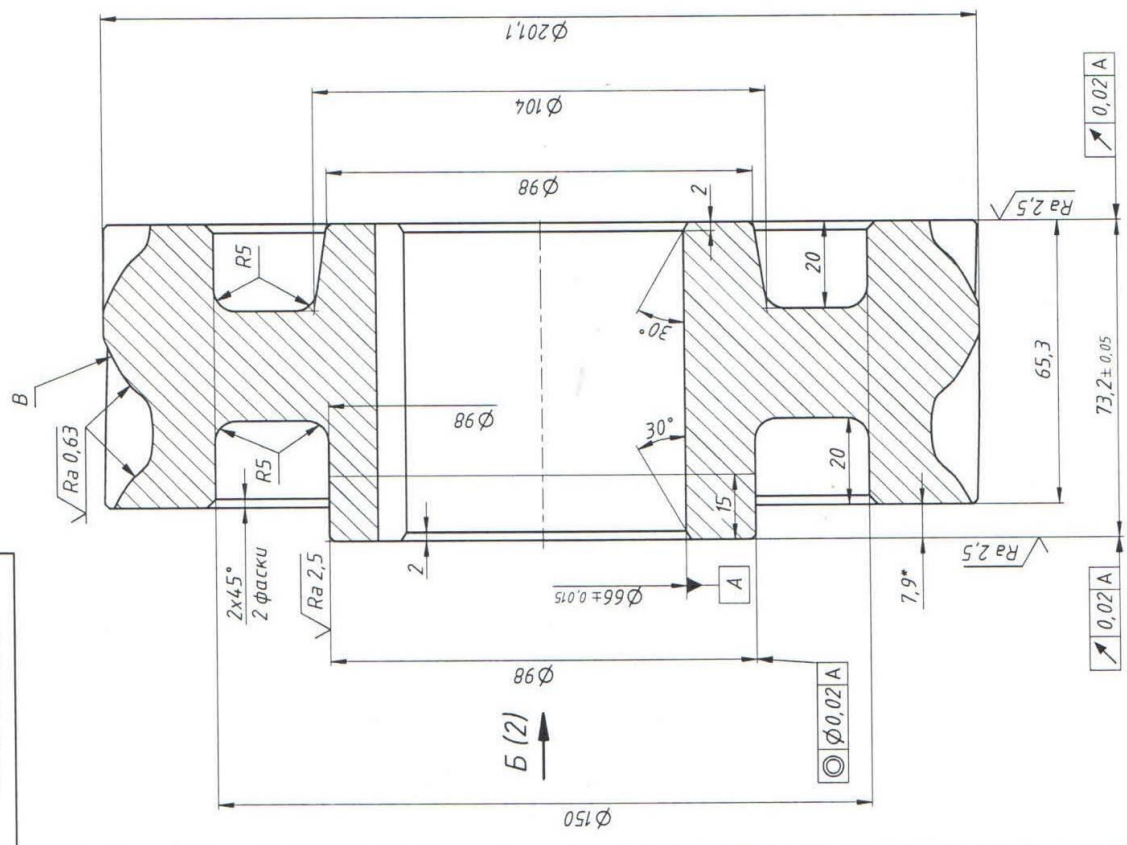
Чертеж колеса выходного редуктора с ЭЦ зубчатым зацеплением
